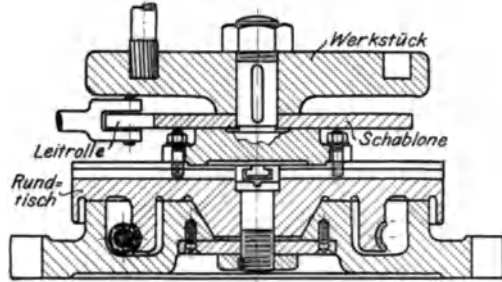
Kopiervorrichtung für Senkrechtfräsmaschinen.
